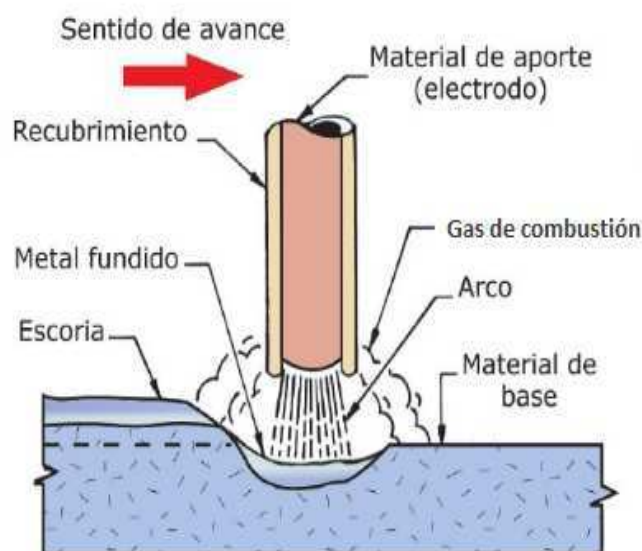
Soldadura Con Electrodo Recubierto
